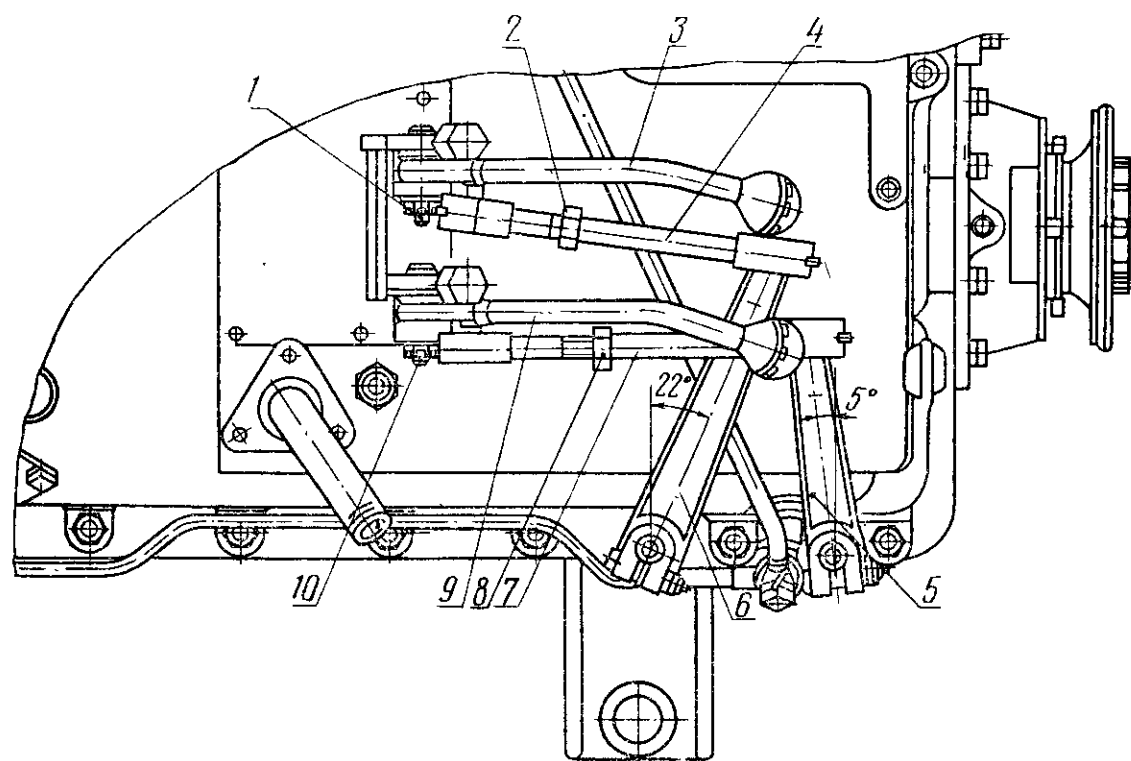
Привод управления муфтами раздаточного вала и включения заднего моста:
